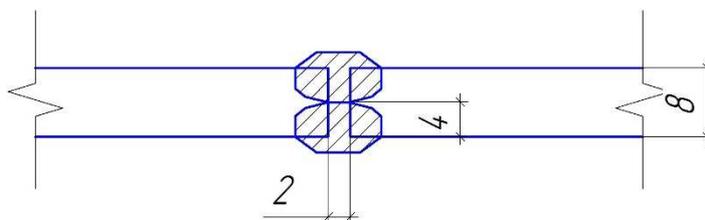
Сварка стыковых соединений толщиной до 8 мм
